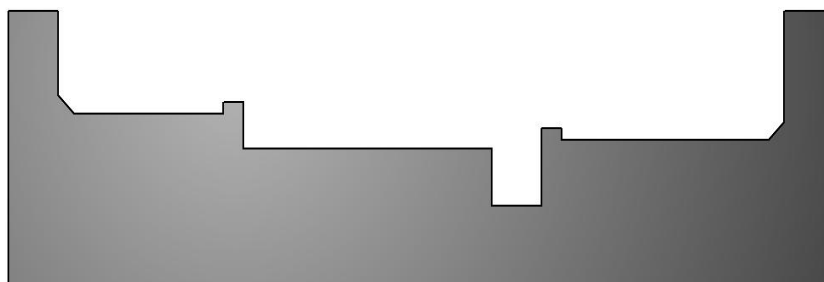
Копир для изготовления вала на токарном копировальном станке
